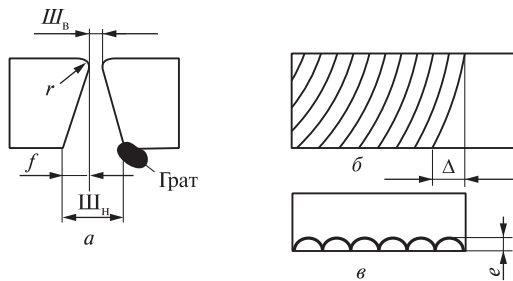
Основные параметры реза при разделяемой кислородной резке: a – поперечное сечение реза; b – вид поверхности реза; e – вид сверху вдоль реза; $Ш_в$ – ширина реза вверху; $Ш_н$ – ширина реза внизу; f – неперпендикулярность реза; e – глубина бороздок – показатель шероховатости реза; Δ – отставание; r – радиус оплавления верхней кромки
